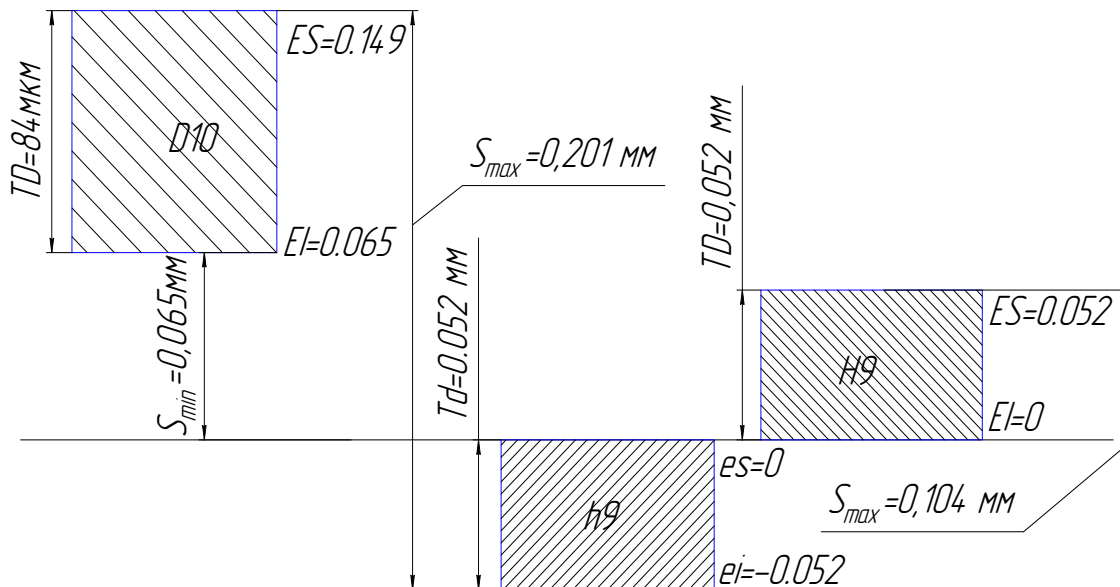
Схема розташування полів допусків вільного шпонкового з'єднання
